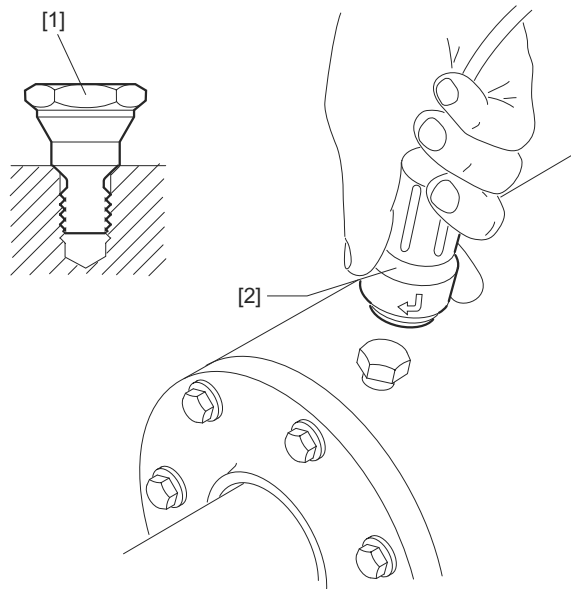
Montage des Stoßimpulssensors am SPM-Adapter
